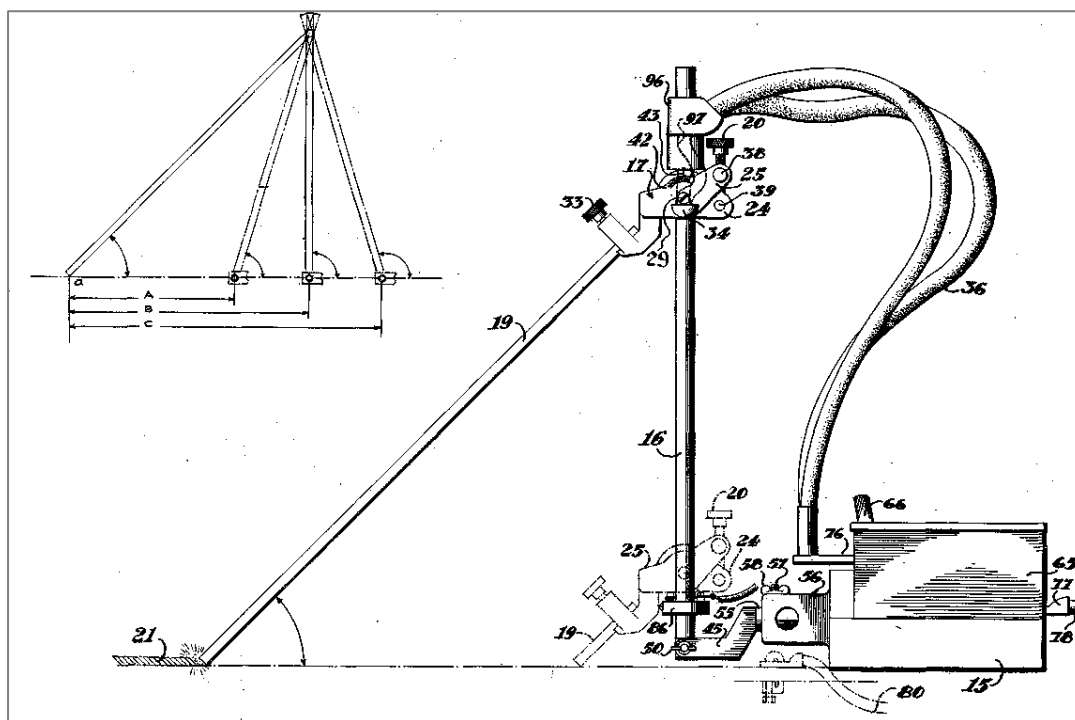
Устройство электроддержателя для сварки
